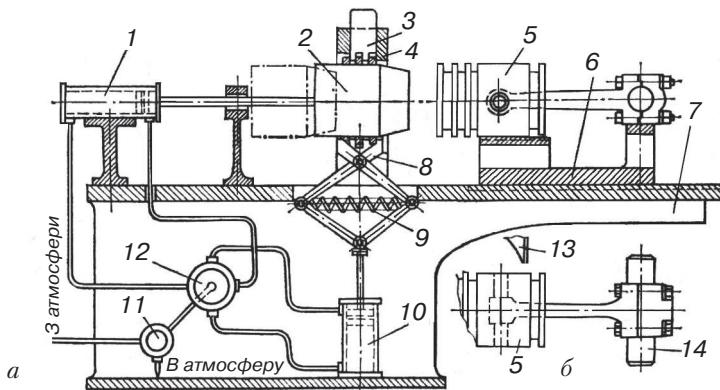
Робочий пристрій для встановлення кілець на поршень:
